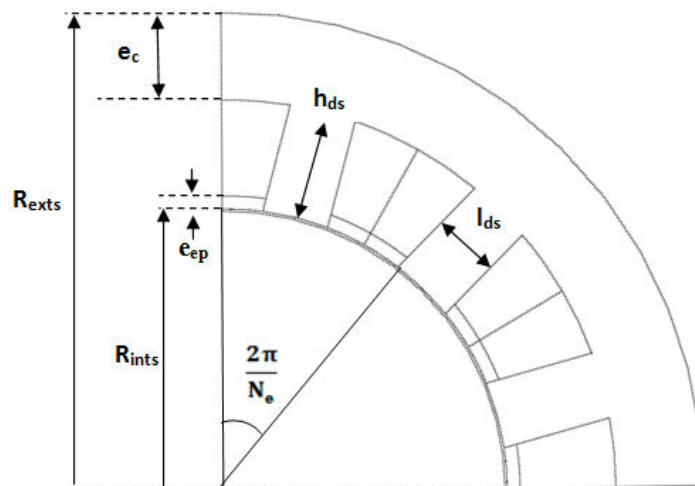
Dimensions géométriques du stator de la machine étudiée
